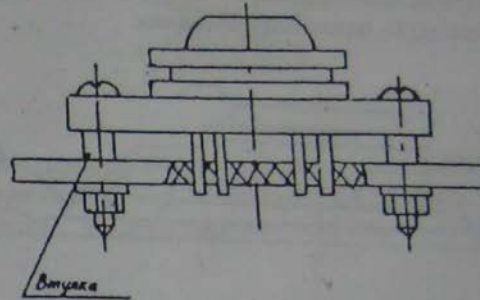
Установка ИМС со штыревыми выводами на печатной плате с дополнительным механическим креплением
